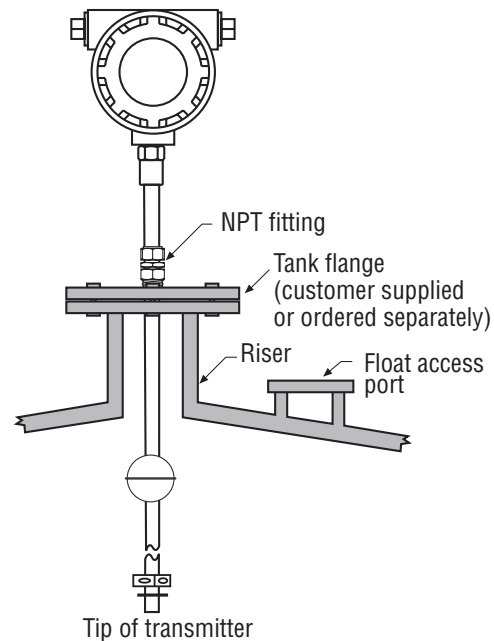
Montagem com rosca fresada para haste rígida e flexível.
